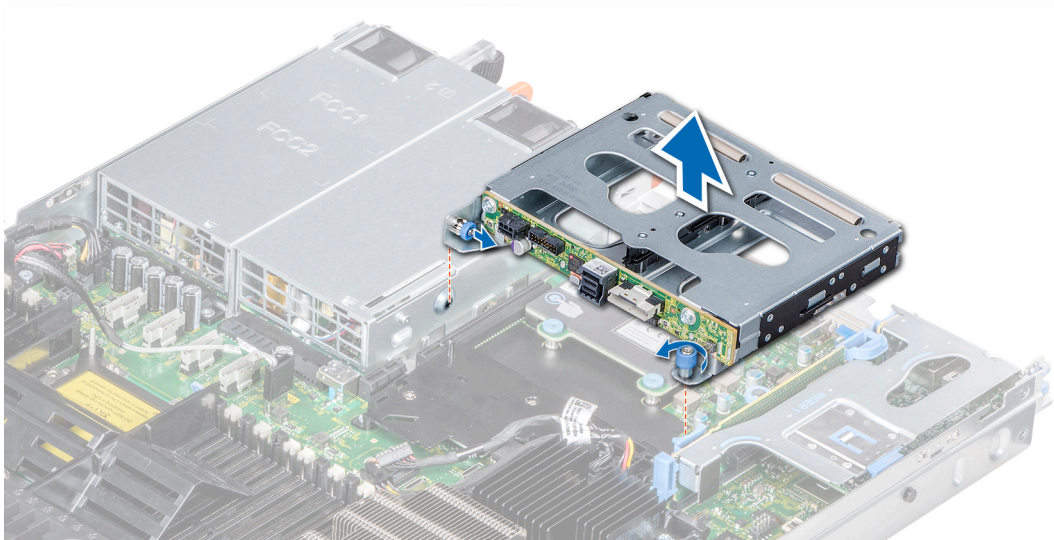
Entfernen des hinteren Laufwerksgehäuses
